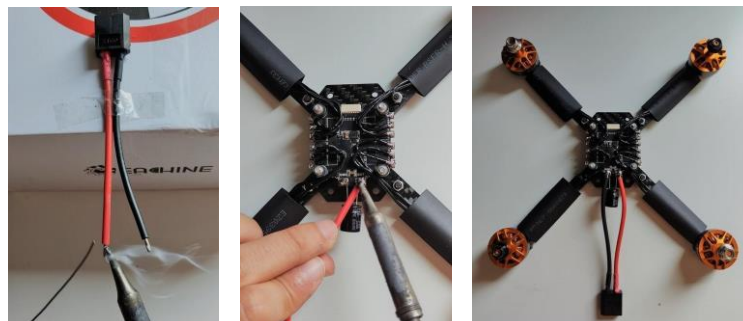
Soldadura del connector d'alimentació. Font: Pròpia
